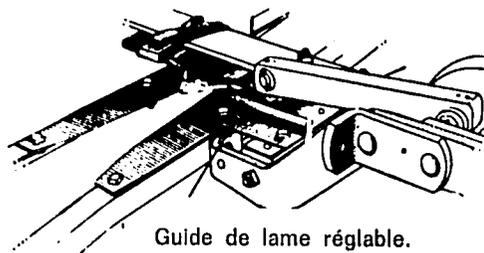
Barre de coupe d'une moissonneuse-lieuse
